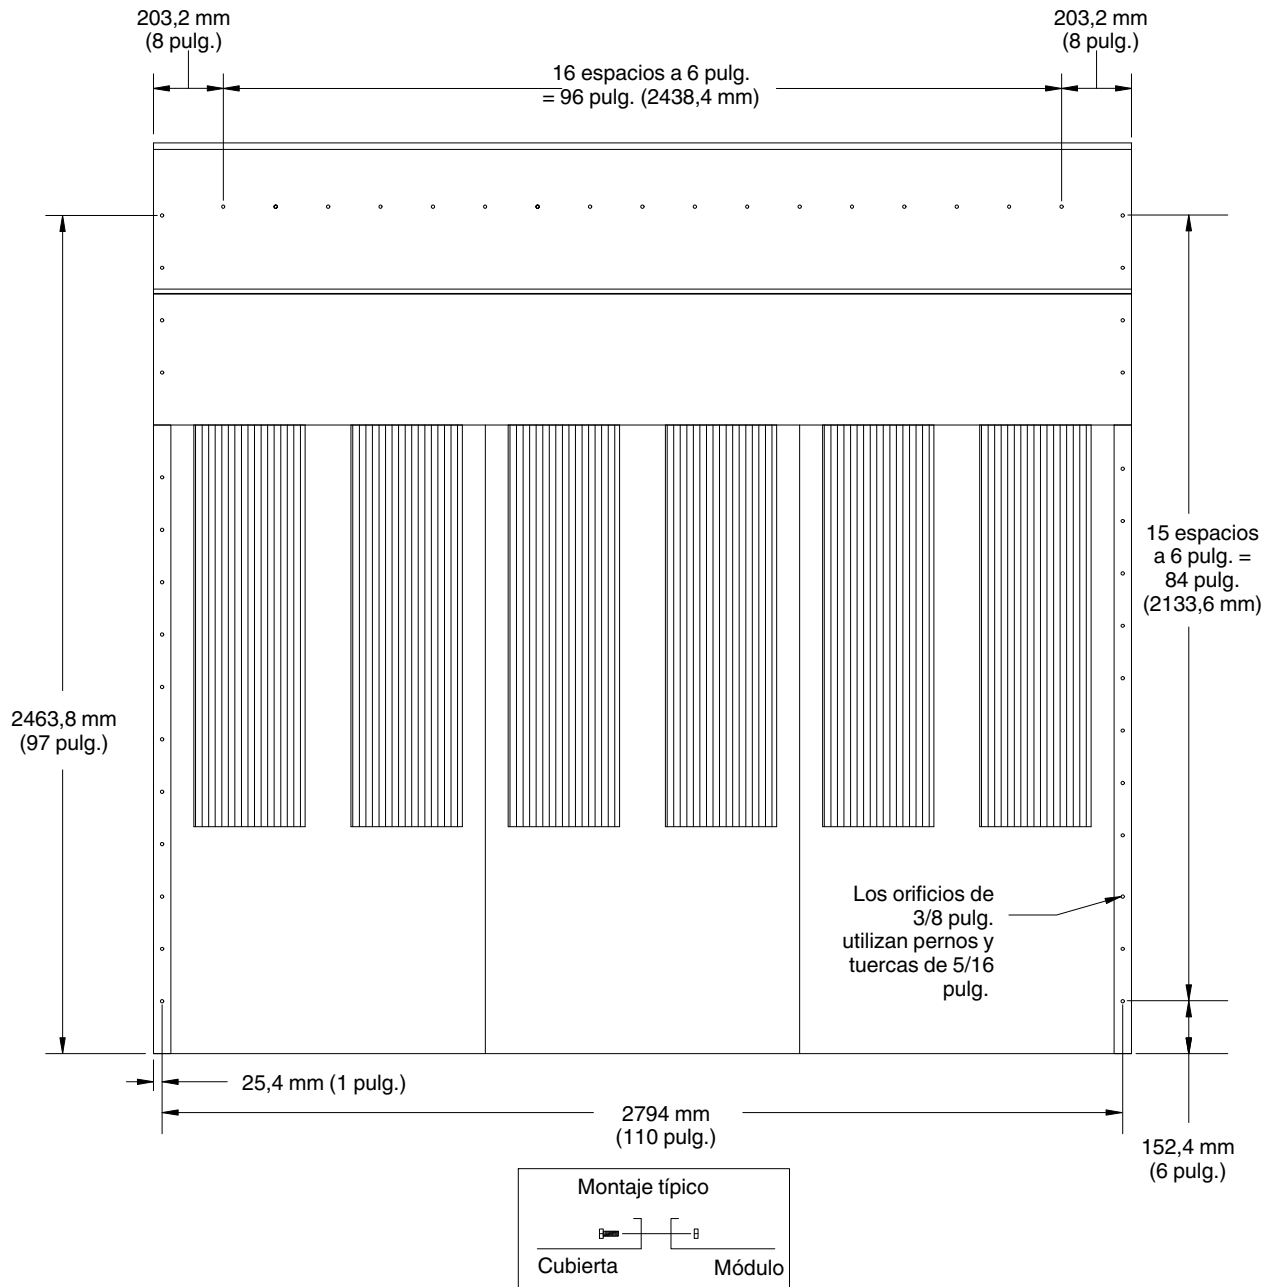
Dimensiones de montaje de módulo de 9.000 pcm a cubierta
